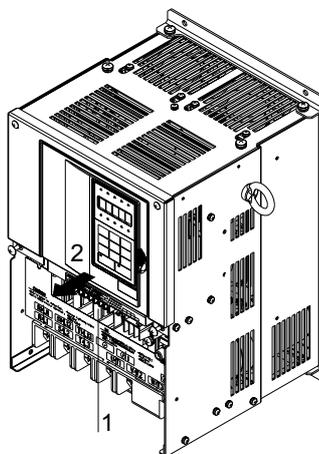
Desmontaje de la tapa frontal (se muestra el modelo CIMR-F7Z2022)
